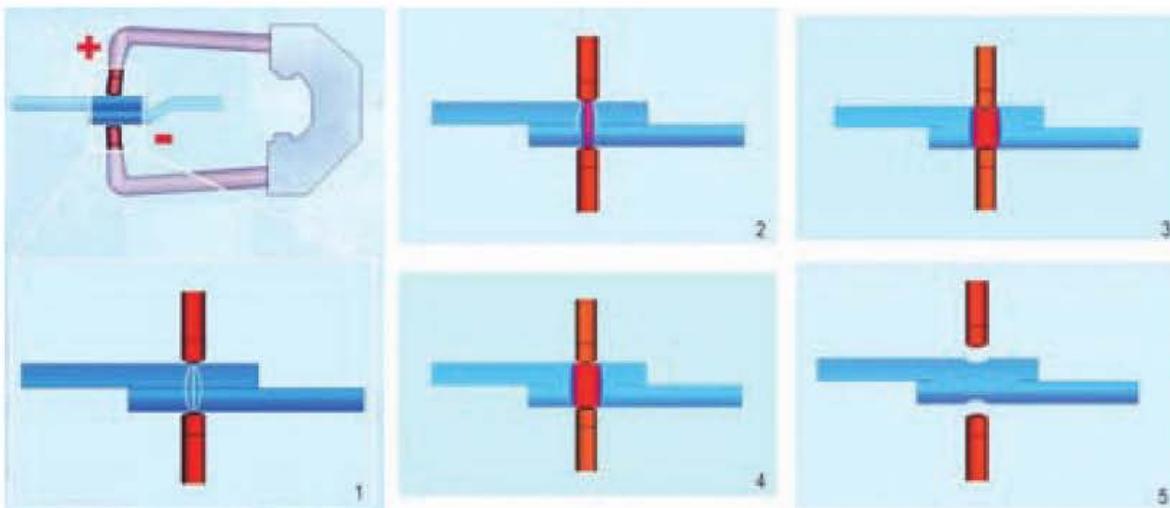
Proceso de la soldadura por resistencia.
